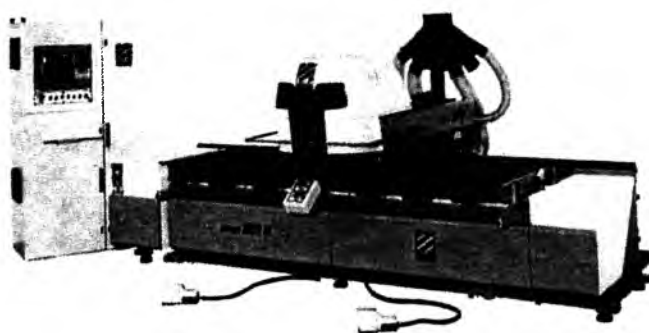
Универсальный обрабатывающий центр с ЧПУ для сверления, фрезерования, шлифования деталей корпусной мебели, фасадов и дверей
